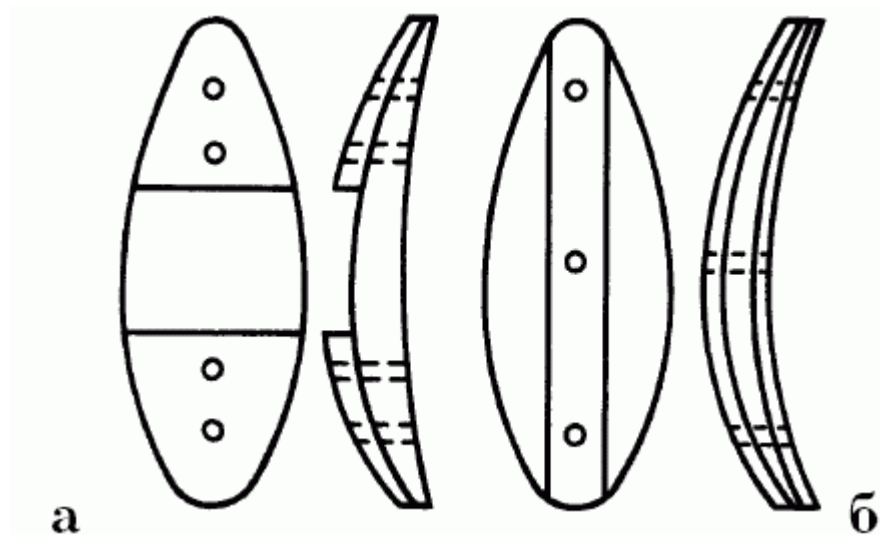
Крепеж накладных поверхностей на плоскость заготовки блесны с помощью заклепок или стержней: – варианты крепежа накладных поверхностей блесны
